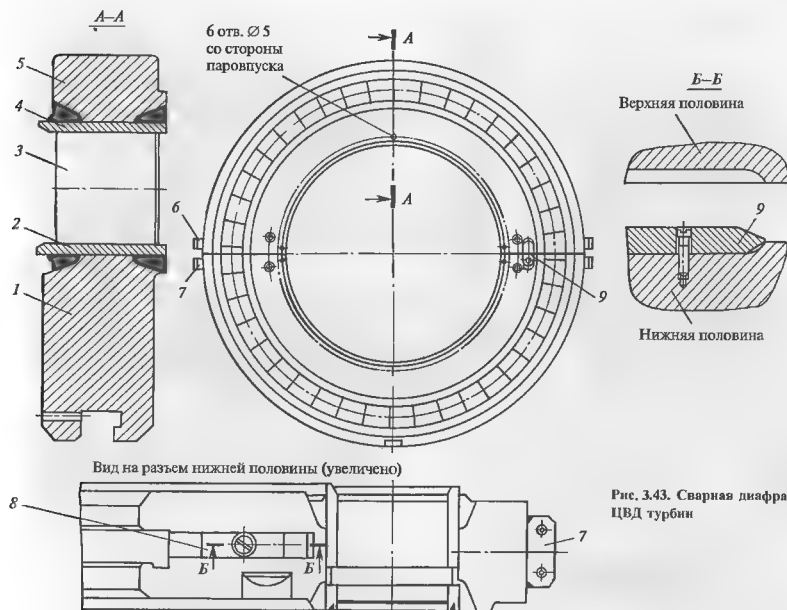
Сварная диафрагма для ЦВД турбин
